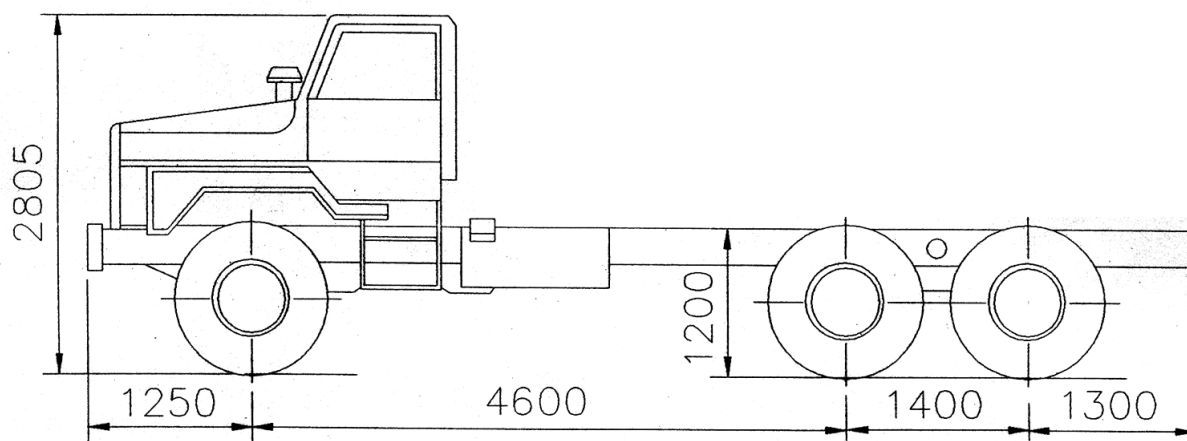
Основные габаритные размеры автомобиля Урал-4320
